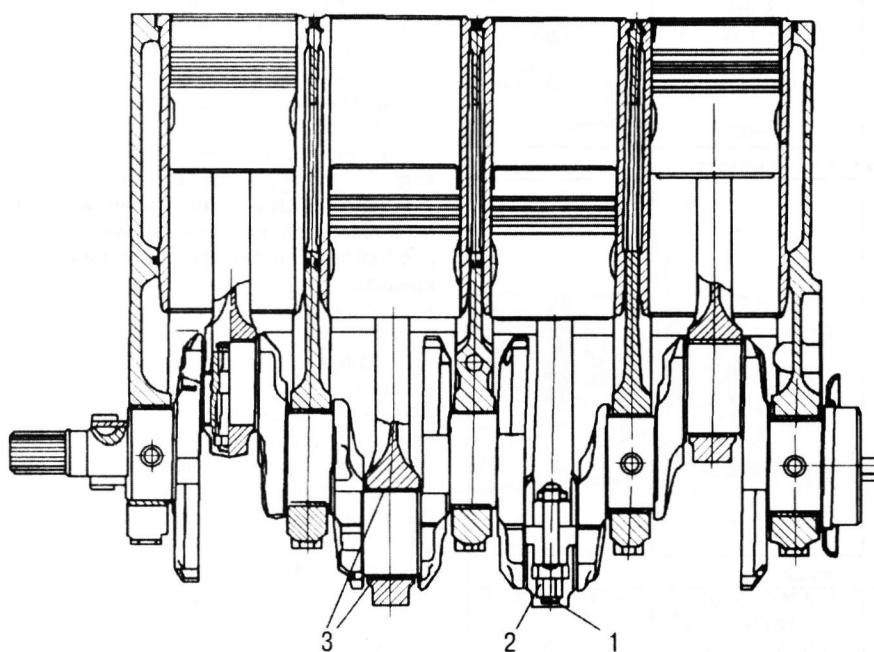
Установка шатунно-поршневой группы: 1 – шатунный болт; 2 – гайка шатунного болта; 3 – шатунные вкладыши
